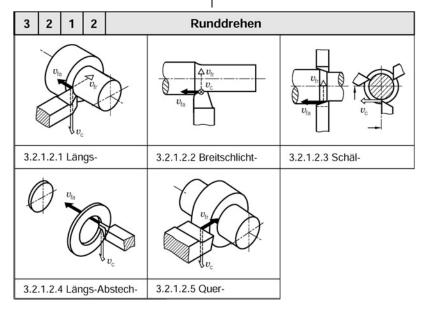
Runddrehverfahren / Procedee de strunjire cilindrică [WES 10]
